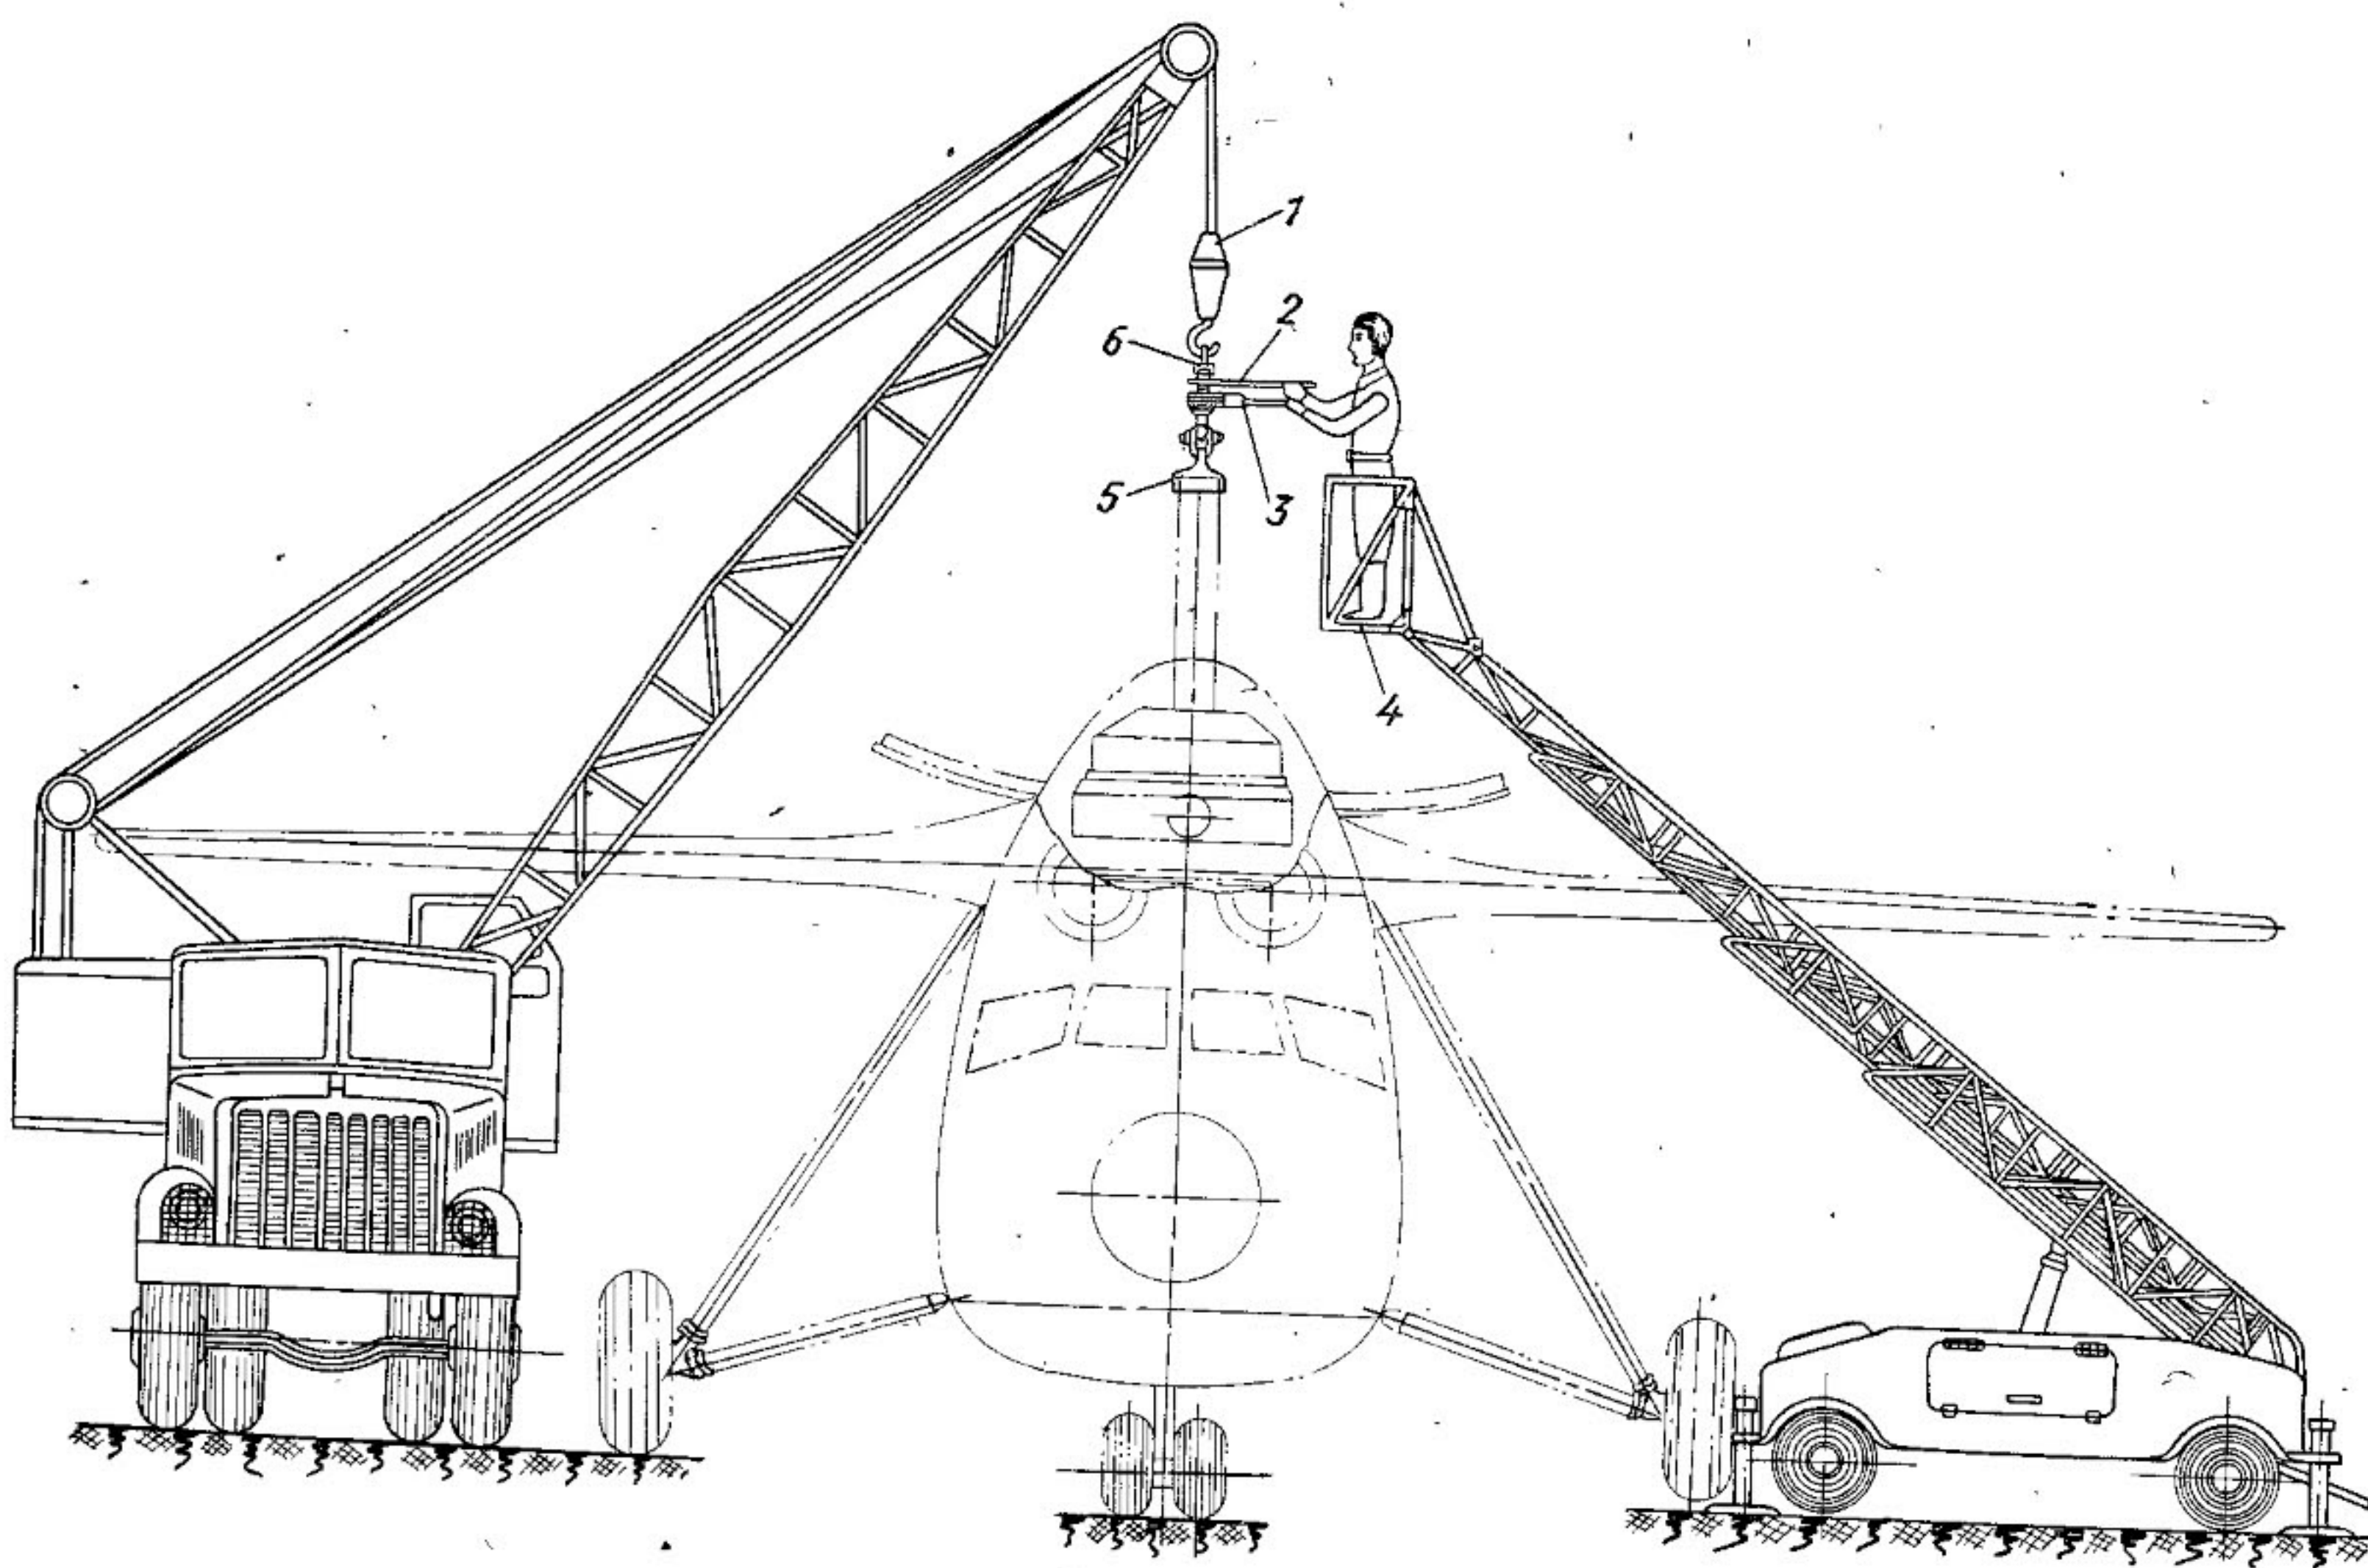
Установка главного редуктора Р-7 при помощи приспособления:
